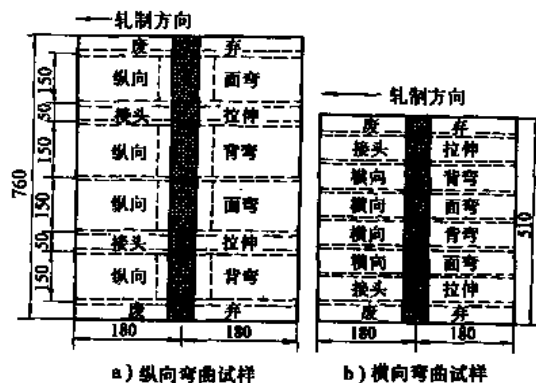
厚度在 9.5mm 及以下的开坡口焊接试板的尺寸和取样部位
